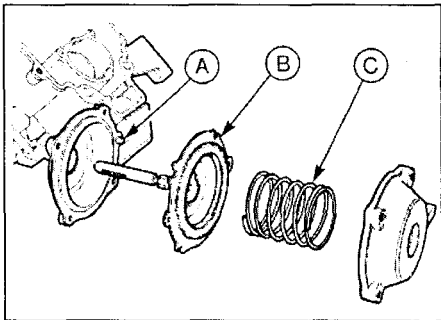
,б. Диафрагменный привод вторичной камеры
